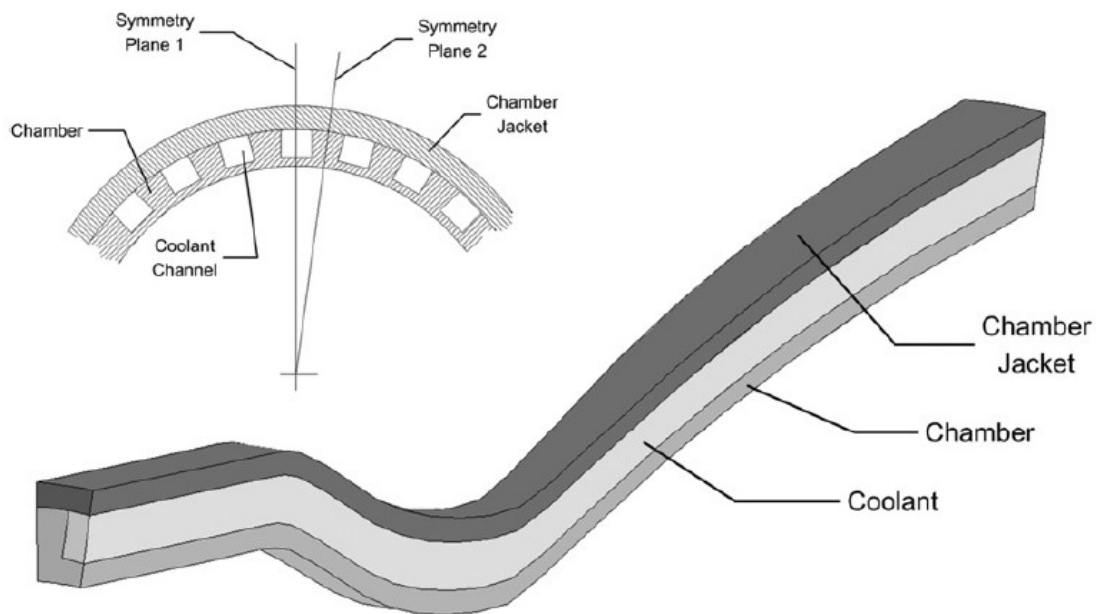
Vista in sezione dei canali di raffreddamento dell'ugello
